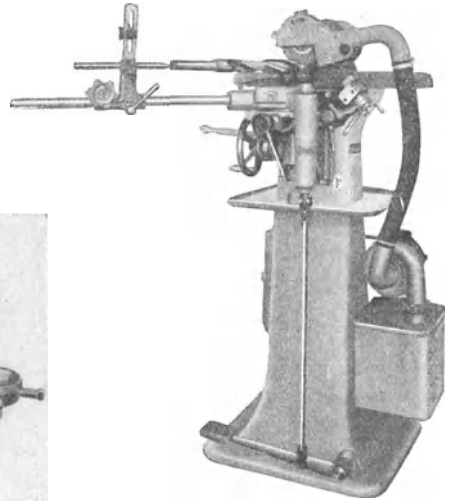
Spiralbohrer-Ausspitzmaschine.
